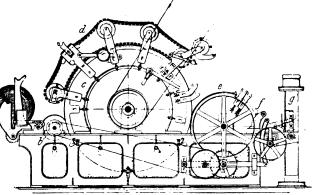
Baumwollkrempel mit wandernden Deckeln.
